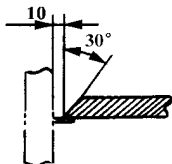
T 形全焊透焊缝坡口尺寸
